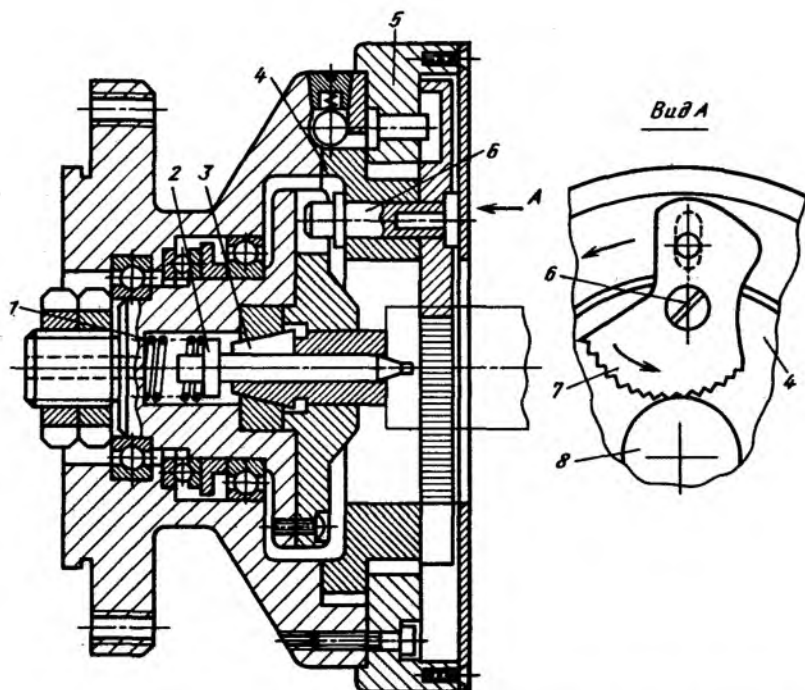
Поводковый патрон с креплением заготовки силами резания
